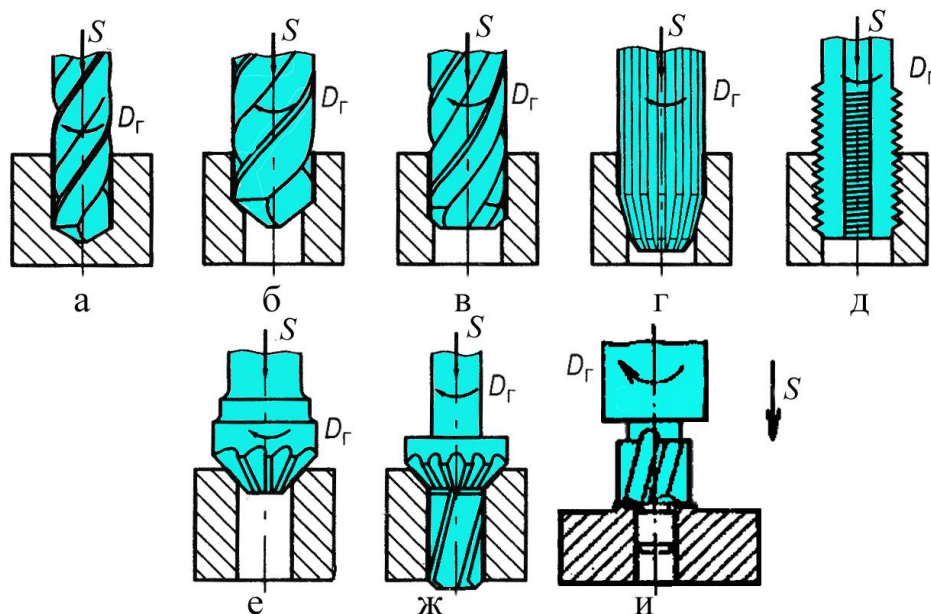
Види робіт, які можна виконувати на свердлильних верстатах: а – свердління; б – розсвердлювання; в – зенкерування; г – розвертування; д – нарізання внутрішньої різі мітчиком; е – зенкування конічної поверхні в отворі; ж – обробка циліндричної та конічної поверхонь в отворі комбінованим інструментом зенкер-зенківка; и – цекування; D_r – головний рух різання; S – рух подачі
